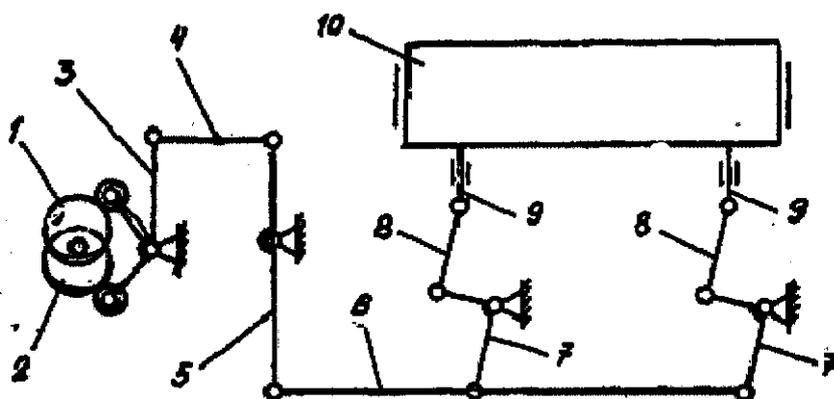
Кулачковый зевобразовательный механизм станков СТБ
